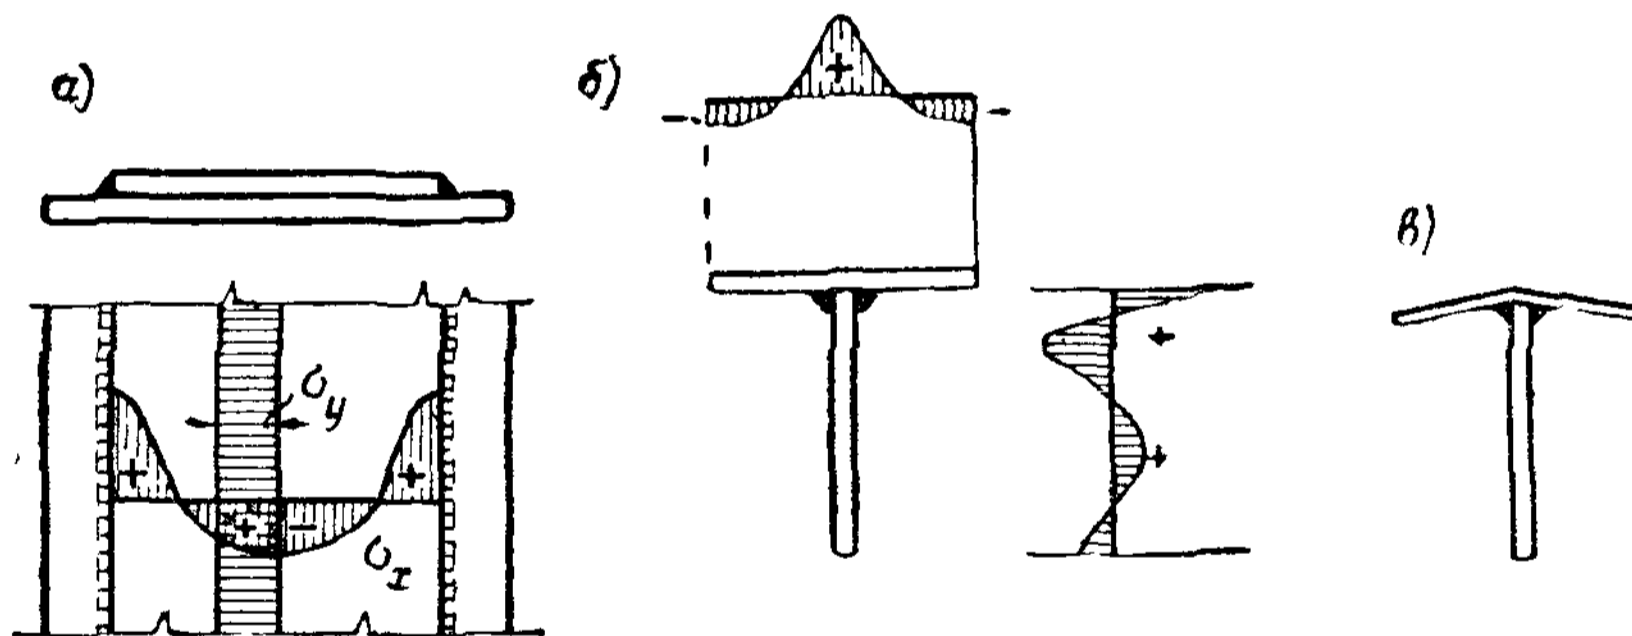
Сварочные напряжения угловых швов в элементах конструкции
